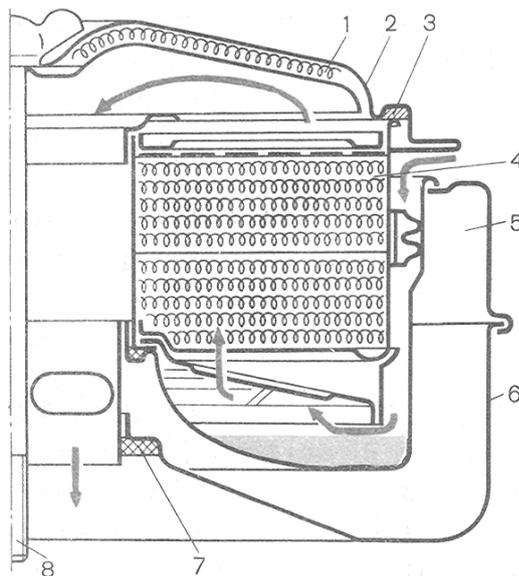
Комбинированный мокрый воздушный фильтр двигателей ЯМЗ-236 и ЯМЗ-238: 1 – шумопоглотитель; 2 – крышка; 3 и 7 – прокладки; 4 – фильтрующий элемент; 5 – камера глушения шума впуска; 6 – корпус; 8 – стержень крепления воздушного фильтра;
